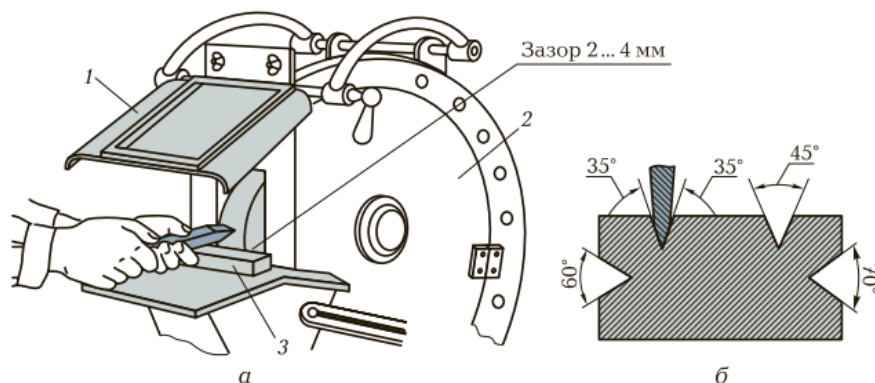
Рабочая зона точильно-шлифовального станка (а) и шаблон для контроля углов заточки (б): 1 — защитный экран; 2 — кожух; 3 — подручник
